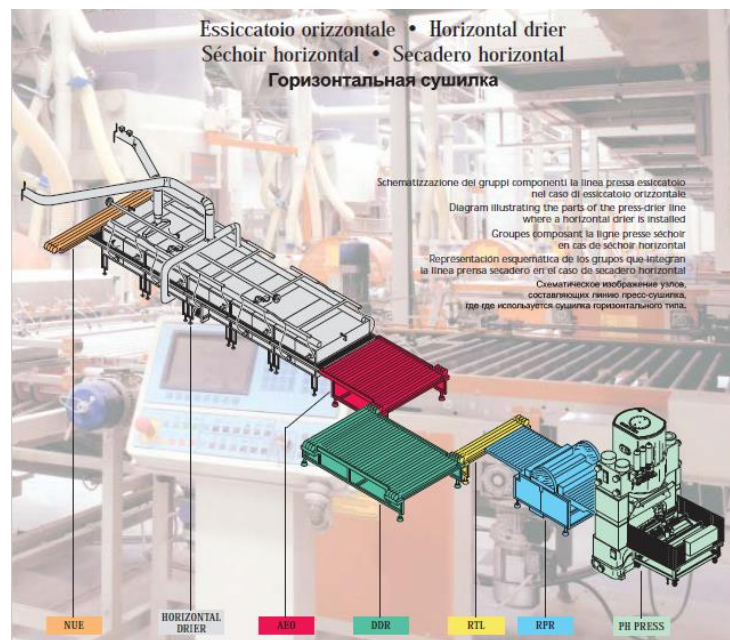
Esquema de conexión entre prensa y secadero horizontal
